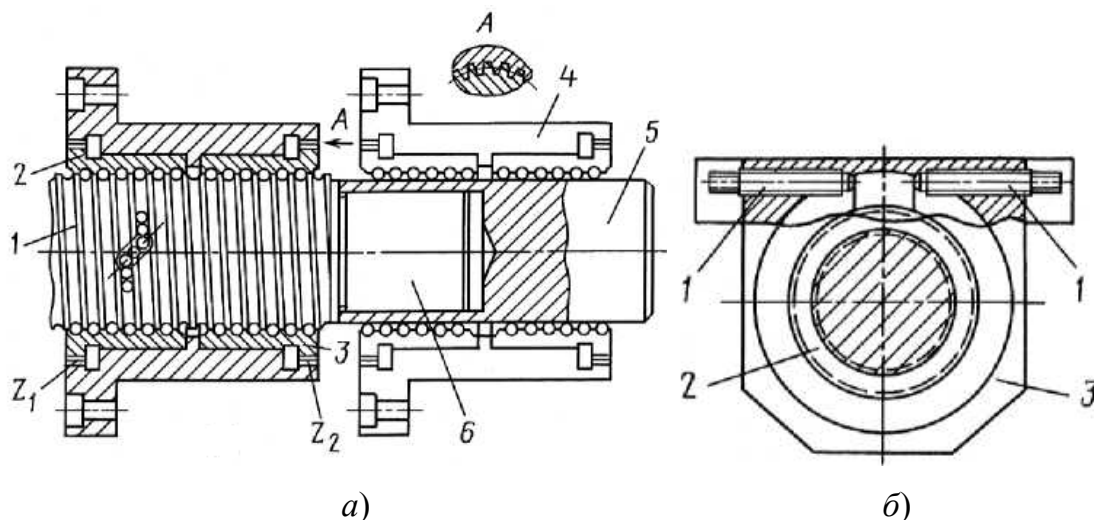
Конструкции устройств регулирования зазоров передач винт-гайка качения:
